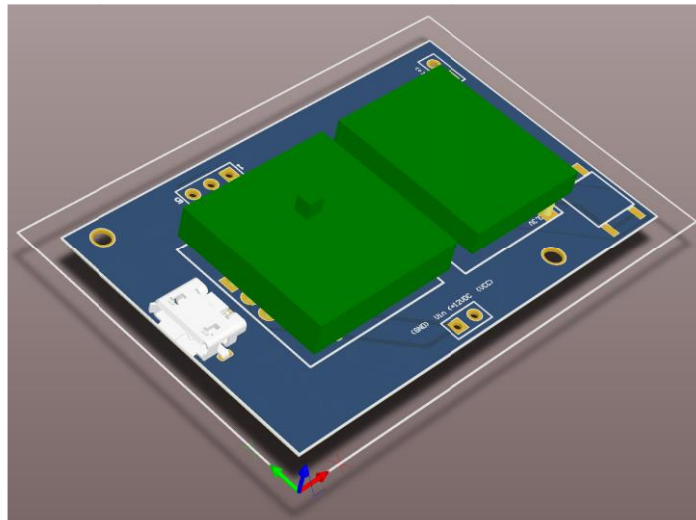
Resultado del PCB Final en perspectiva visto desde la Capa Superior [20]
